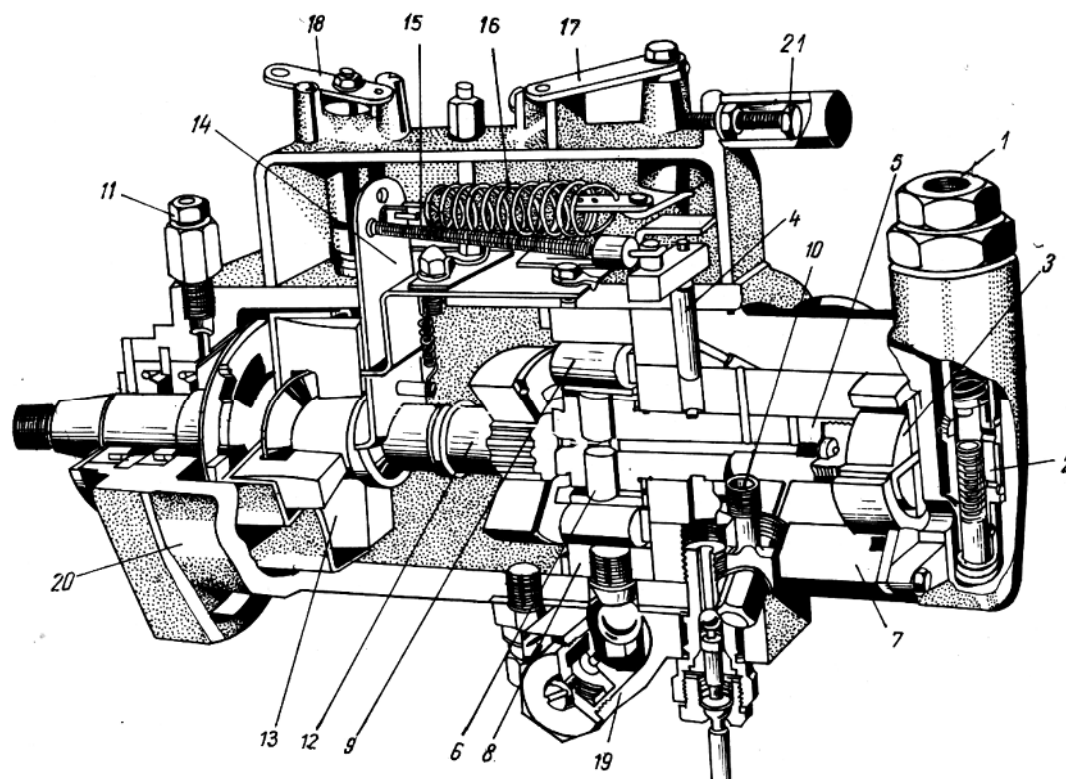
,a – Pompa de injecție rotativă (DPA – CAV):
